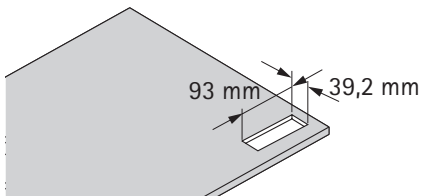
Fräsbild zum Einbau des Handschalters LegaDrive Touch Inlay mit Gummilamellen
